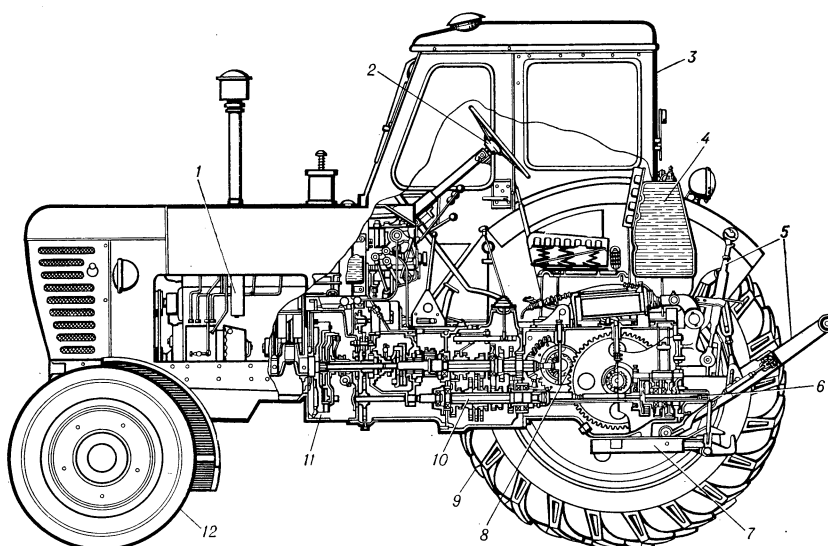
Продольный разрез колёсного трактора: 1 — двигатель; 2 — рулевое колесо; 3 — кабина; 4 — топливный бак; 5 — рычаги навесного устройства; 6 — вал отбора мощности; 7 — сцепный крюк; 8 — центральная передача; 9 — ведущее колесо; 10 — коробка передач; 11 — муфта сцепления; 12 — направляющее колесо.
